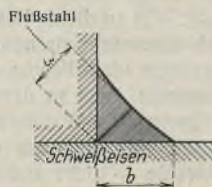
Schweißquerschnitts-abmessungen.
